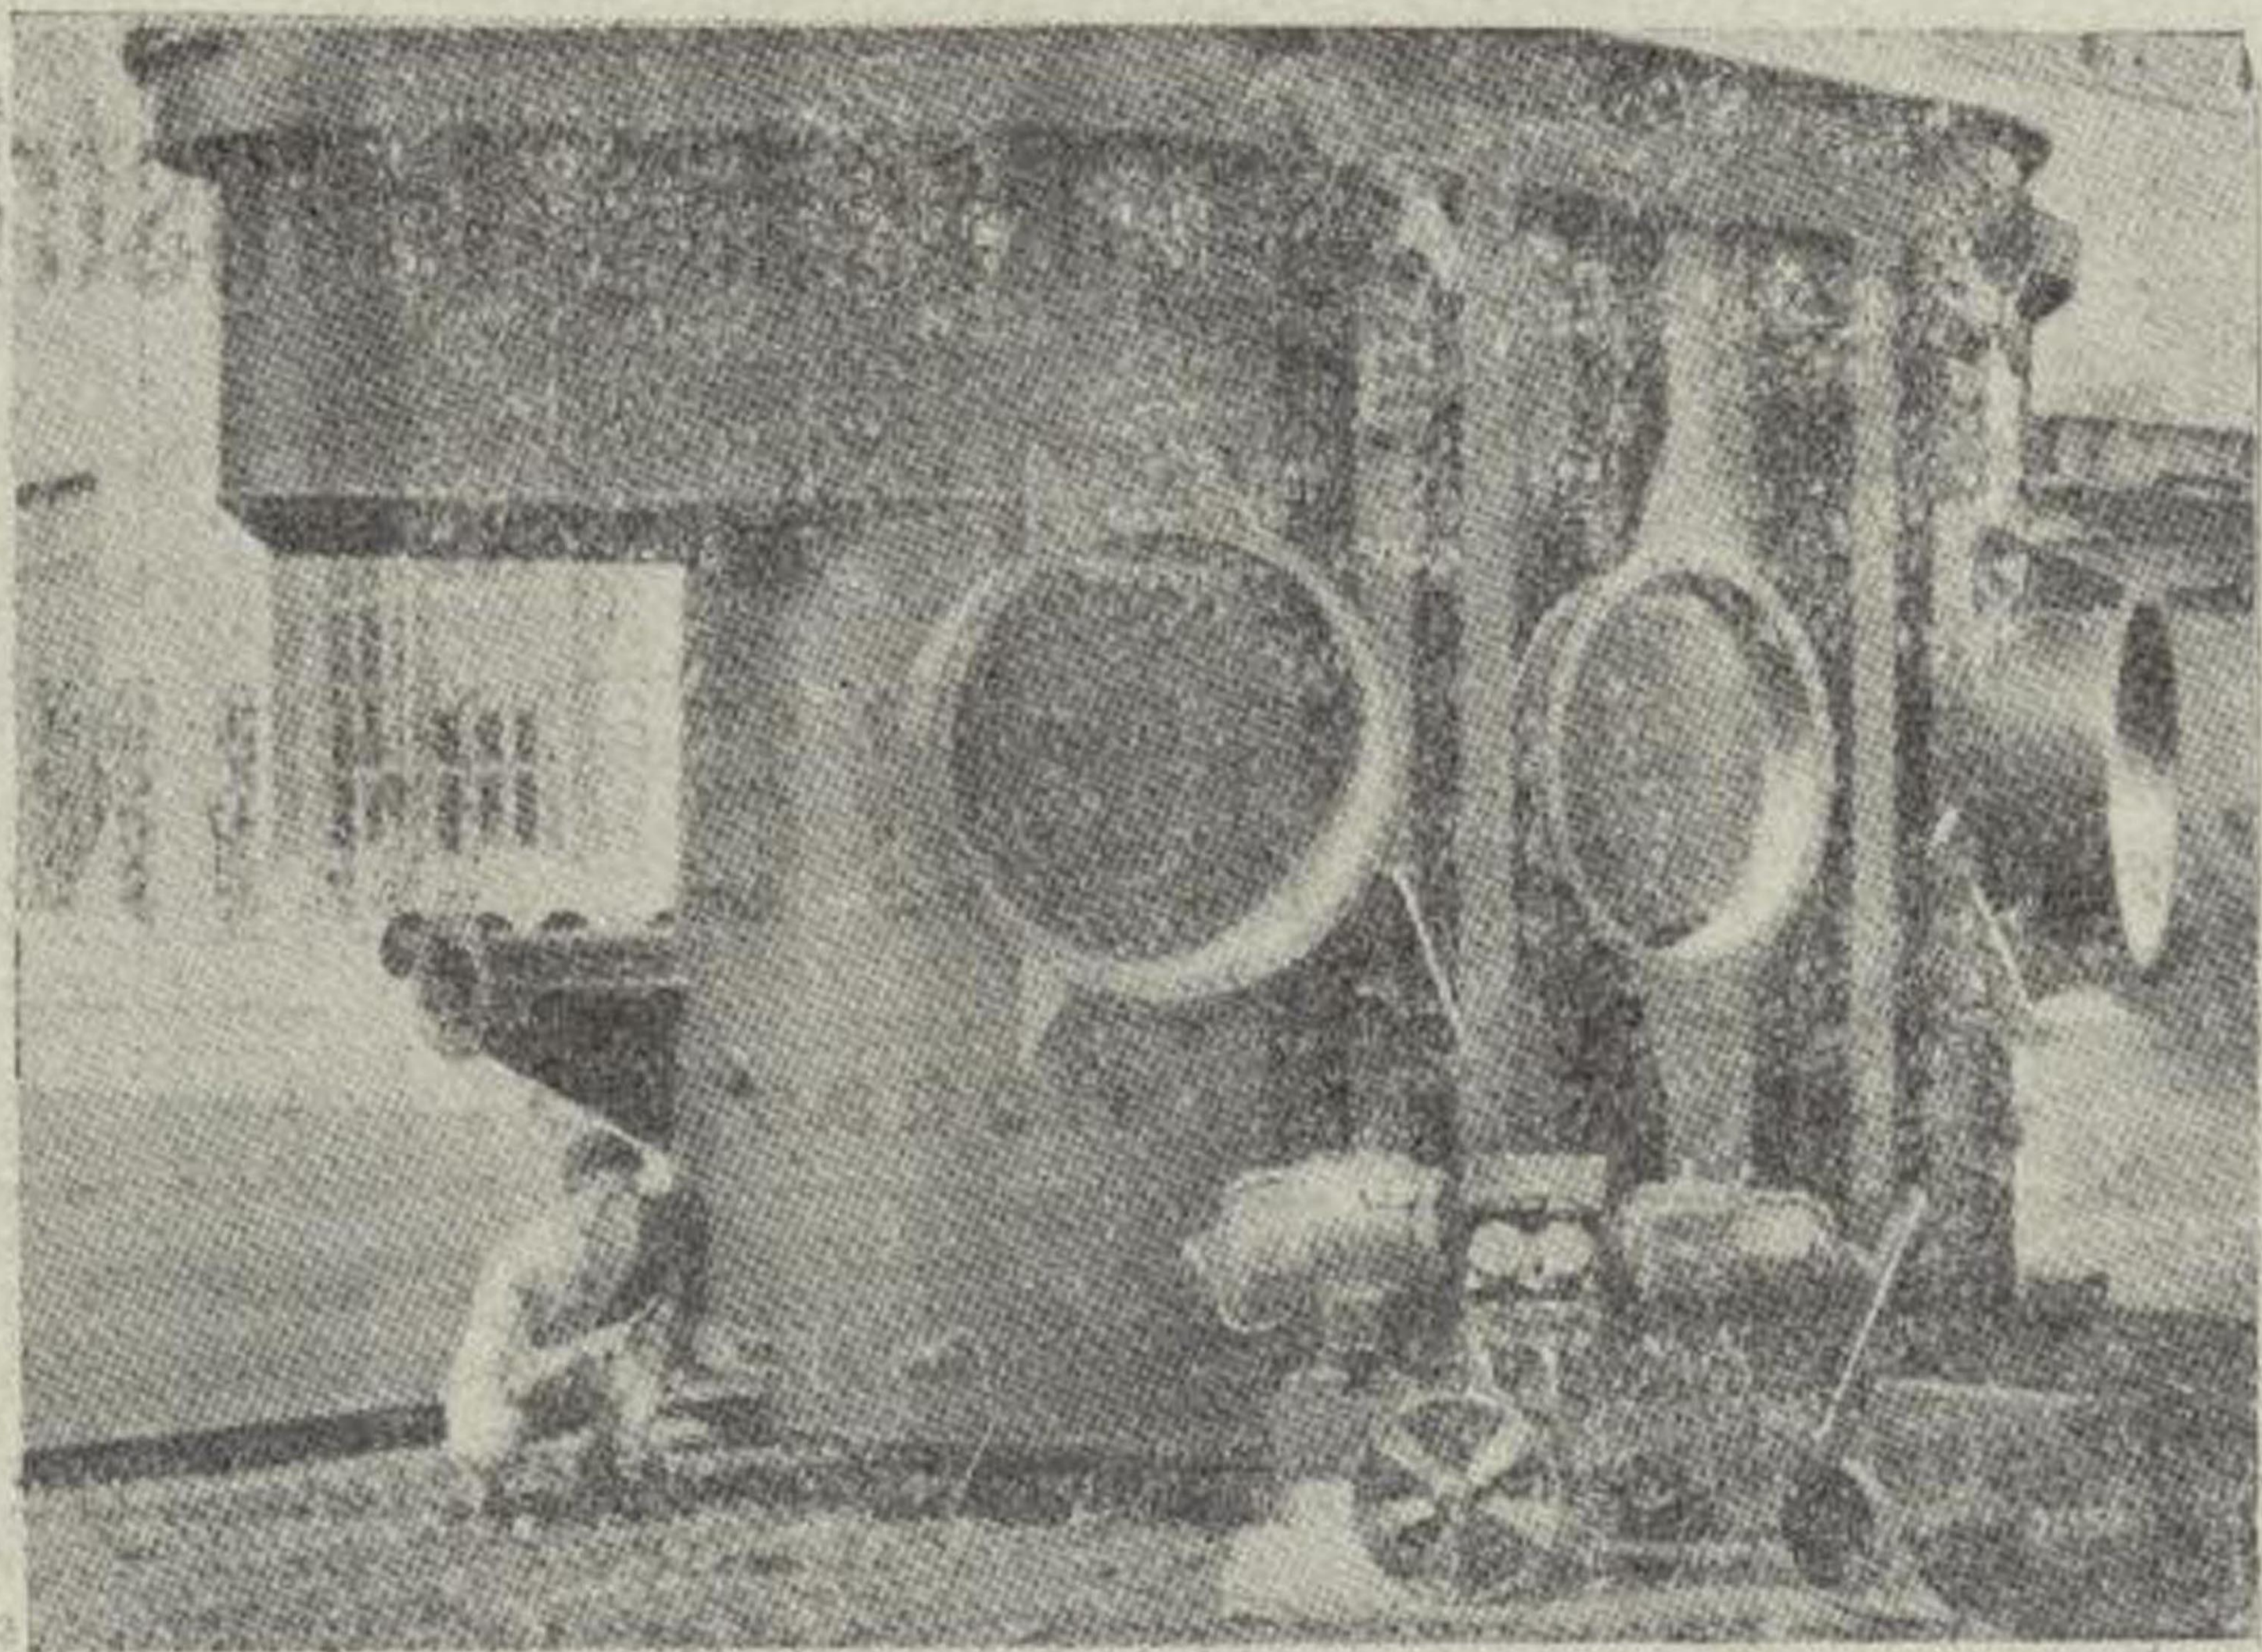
^a—Grupo de soldadura universal para un soldador.
